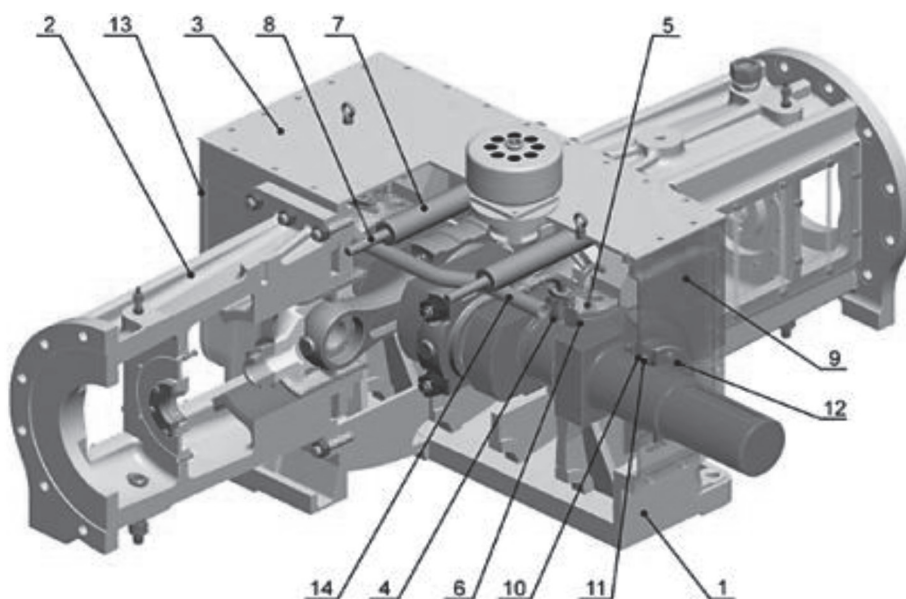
Оппозитная база 2М10А быстроходного компрессора 2ГМ10А-2,7/21-151: 1 – картер; 2 – направляющая; 3 – крышка картера верхняя; 3 – вкладыш; 4 – крышка подшипника; 6 – полукольцо; 7 – распорка; 8 – стяжка; 9 – крышка маслоснимателя; 10 – манжета; 11 – кольцо; 12 – фланец; 13 – крышка картера передняя; 14 – коллектор смазки коренных подшипников.
